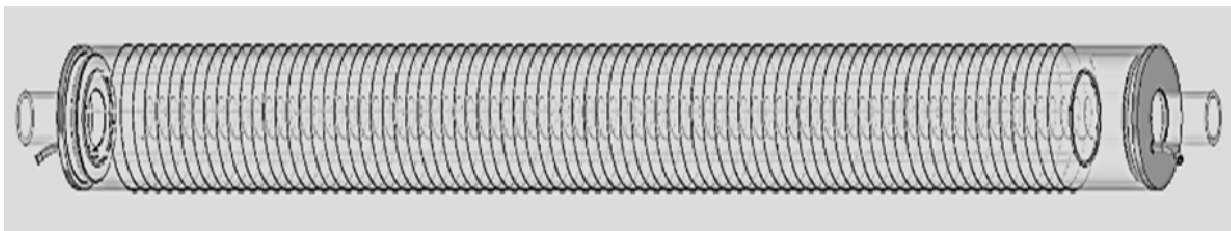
Внешний вид реактора с цилиндрической геометрией
